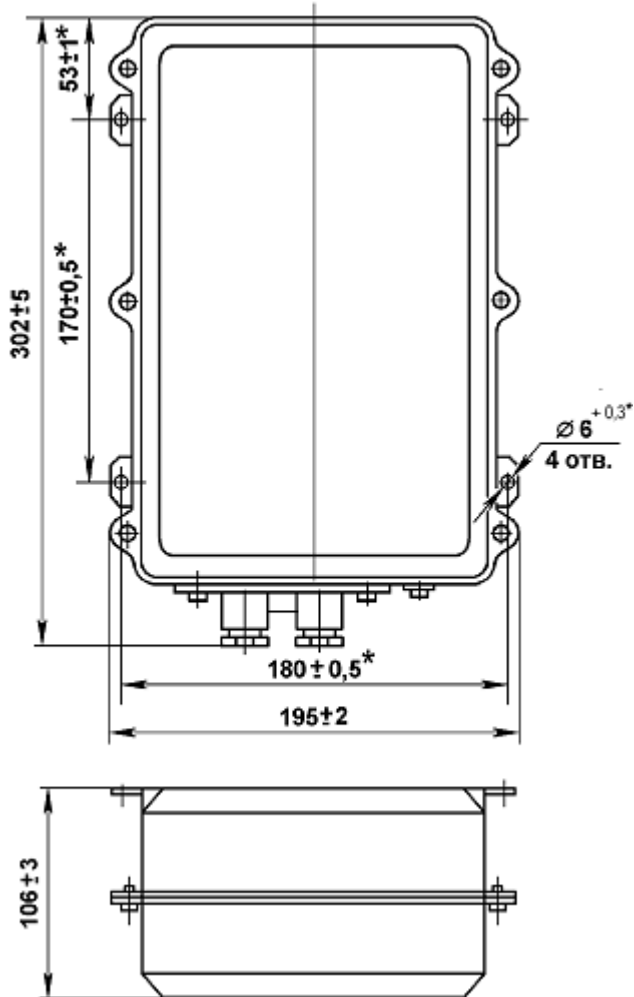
для усилителей ФЦ-0620, ФЦ-0621
